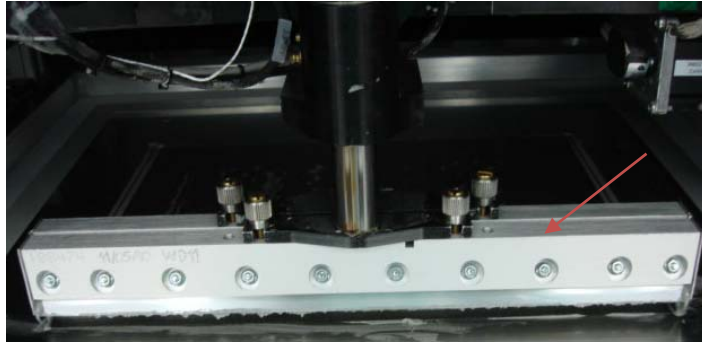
Printing Fixture สำหรับเรียงแผ่นวงจร
